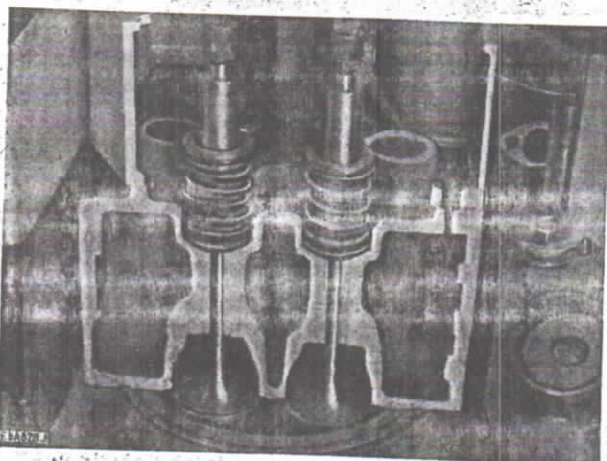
Dieselmotor 8 KVD 21 T, Zylinderkopfschnitt
